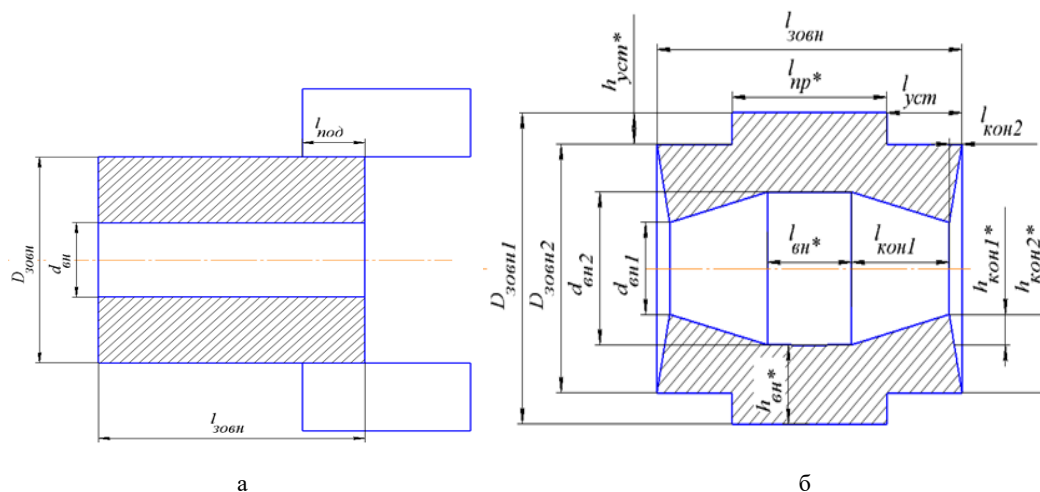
Заготовка до початку кування (а), кована поковка (б)
